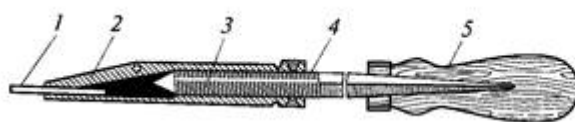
Шабер со сменными режущими пластинами: 1 — режущая пластина; 2 — держатель; 3 — корпус; 4 — зажимной винт; 5 — рукоятка
